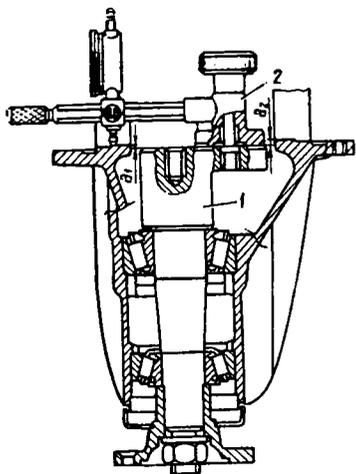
Схема снятия замеров для определения толщины регулировочного кольца ведущей шестерни: 1 - оправка А.70184; 2 - приспособление А.95690 с индикатором; а₁ и а₂ - расстояния от торца оправки до шеек подшипников дифференциала
